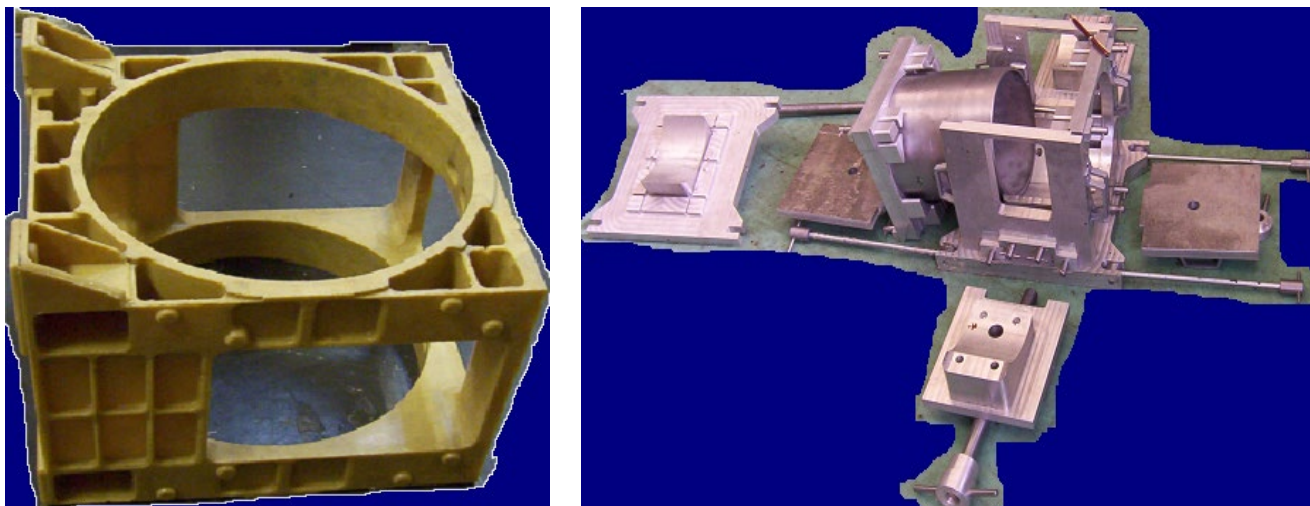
Пресс-форма и восковая модель детали «Корпус»
